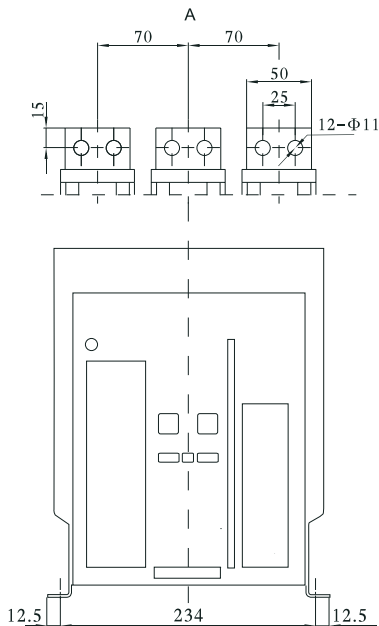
Габаритные размеры выдвижных трехполюсных выключателей типоразмера А
